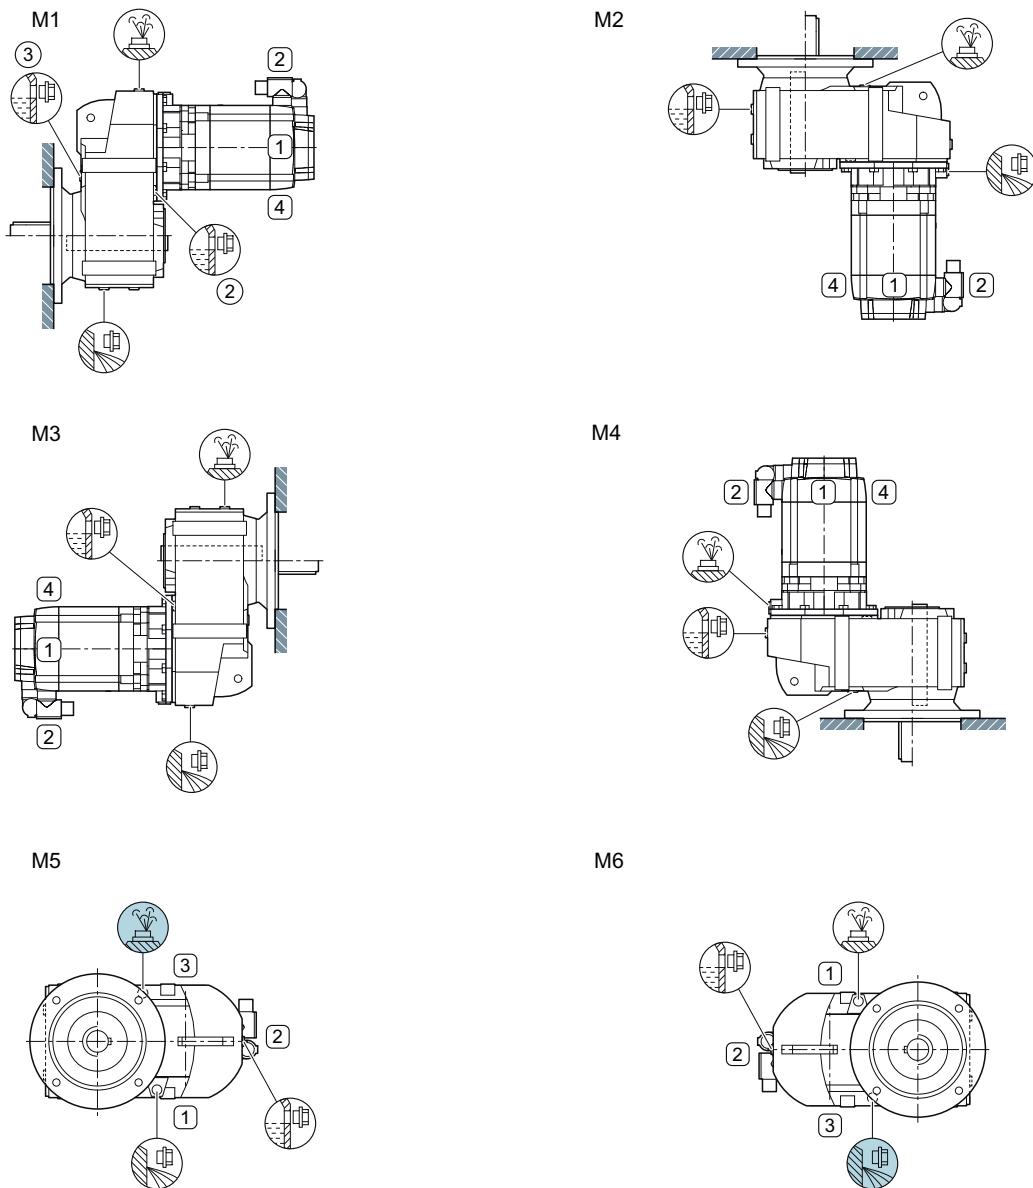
Einbaulagen für Servo-Flachgetriebemotoren FZ.F und FD.F (Flanschausführung) und FZ.Z und FD.Z (Gehäuseflanschausführung), Baugrößen 39 - 129, 2-stufig und 3-stufig
